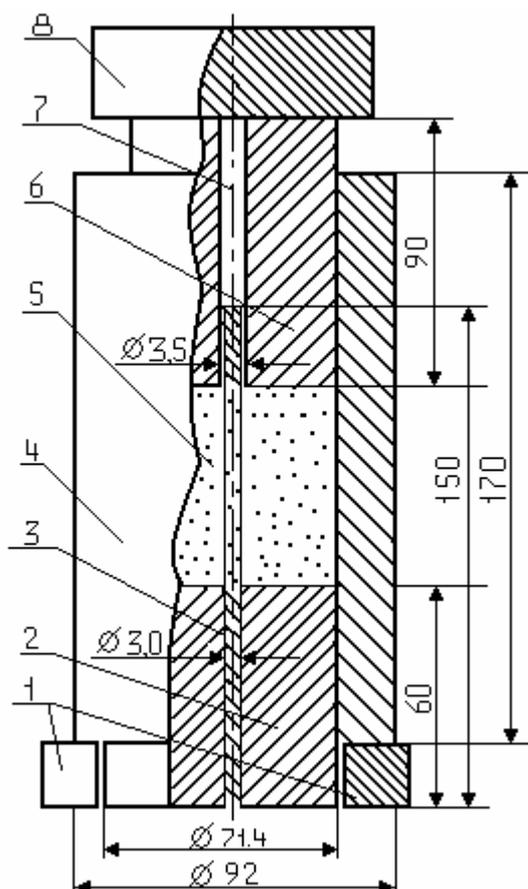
Приспособление для уплотнения образцов из холодных смесей для определения слеживаемости: 1 – подставки; 2 – нижний вкладыш формы; 3 – стальной стержень; 4 – цилиндрическая форма; 5 – образец; 6 – верхний вкладыш формы; 7 – сквозное отверстие; 8 – груз
